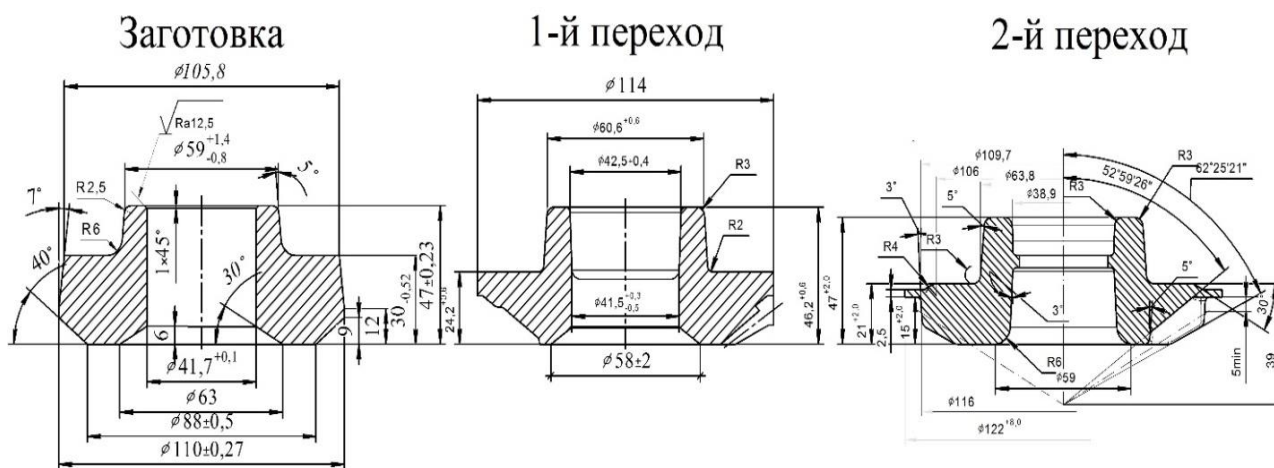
Переходы сферодвижной штамповки конического зубчатого колеса
